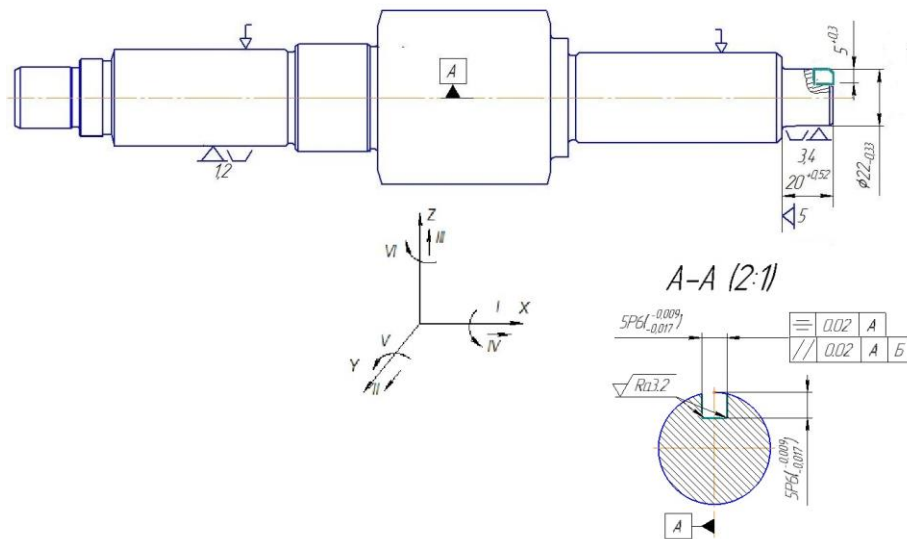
Схема базування в призмах (варіант 2)
